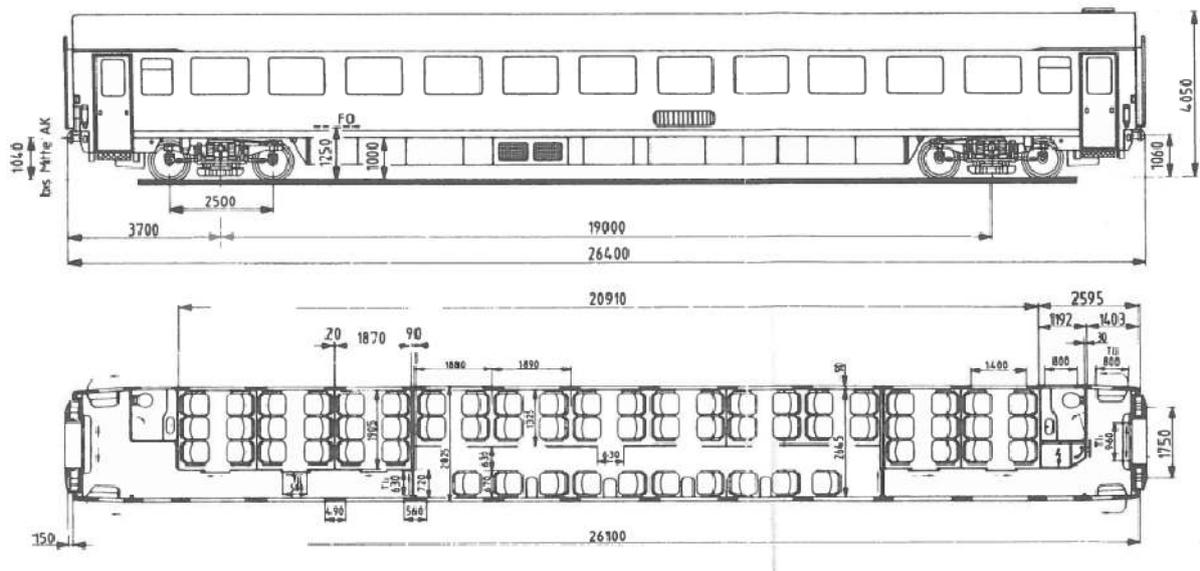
Grundriss und Seitenansicht Bvmz 186.x
